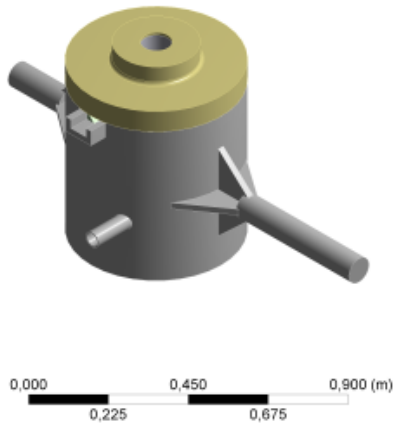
Horno de crisol en el Design Modeler. Fuente: Autor.
